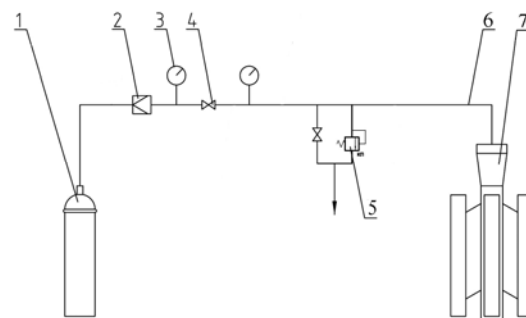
Схема устройства для газодинамического воздействия на расплав в керамической оболочковой форме: 1 – баллон с аргоном; 2 – редуктор; 3 – манометр; 4 – вентиль; 5 – клапан предохранительный; 6 – металлорукав; 7 – литейная форма.
